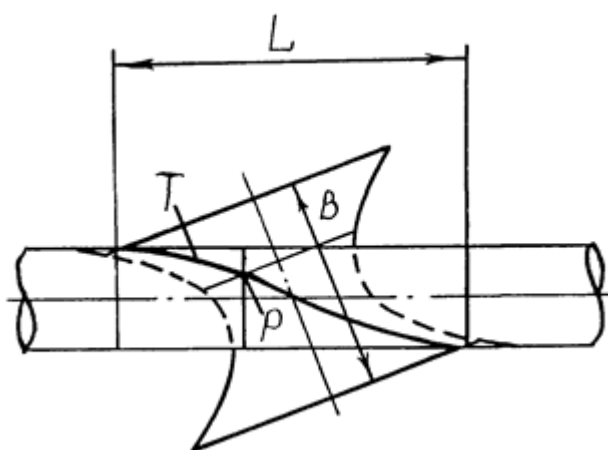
Схема обробки зубців циліндричного зубчастого колеса
